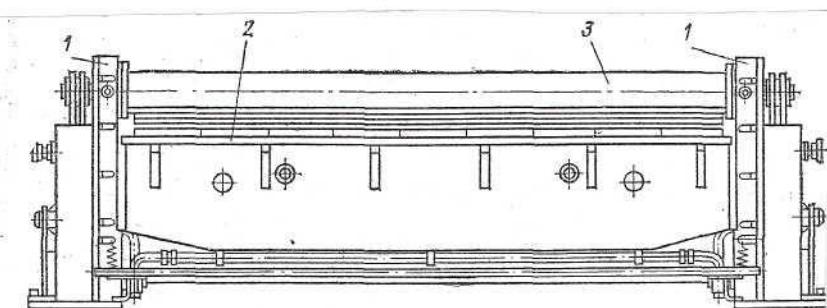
Листогибочный механизм СТД-136 (1 — стойка; 2 — стол; 3 — ножевая балка)
